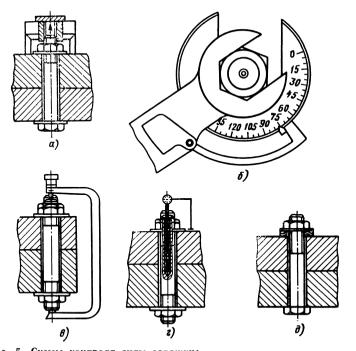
Схемы контроля силы затяжки: a — по осевой силе; b — по углу поворота гайки; b — скобами; b — с помощью индикатора; b — мерными шайбами
